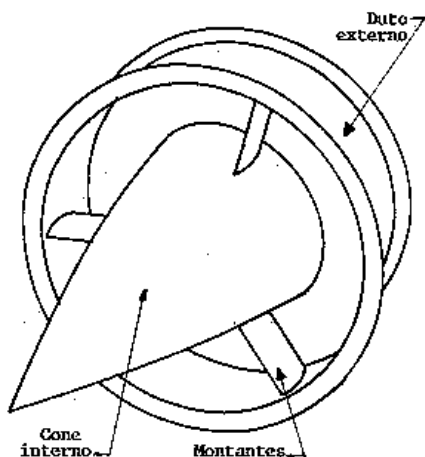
Coletor de escape com suporte soldados.
